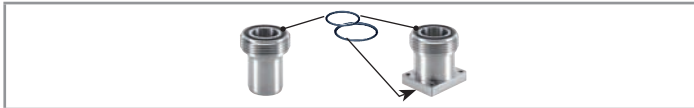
O-Ring-Dichtungen für den Adapter aus Edelstahl
